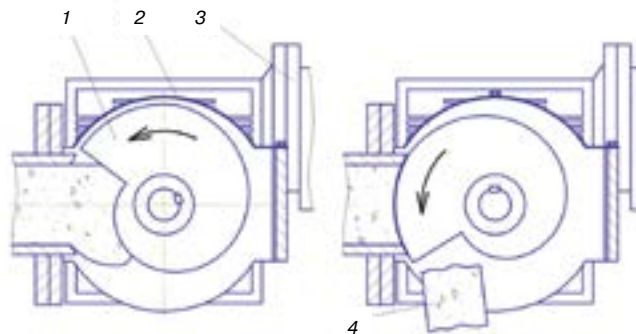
Устройство механизма камнеудаления: 1 – нож; 2 – корпус; 3 – мотор-редуктор; 4 – каменные отходы
